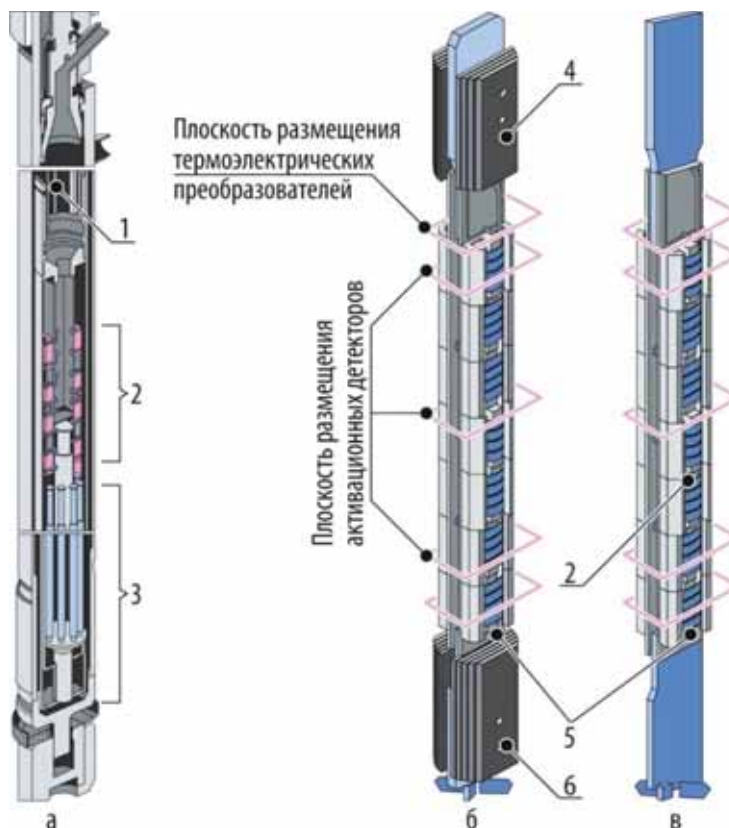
Конструктивная схема I (а), II (б) и III (в) облучательных устройств: 1 — термоэлектрические преобразователи; 2 — нагружающие пеналы; 3 — нагревательный блок; 4 — верхний нагреватель; 5 — держатель; 6 — нижний нагреватель
